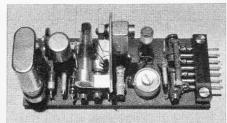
Steckeinheit des Senders mit den Abmessungen 30 mm × 75 mm
